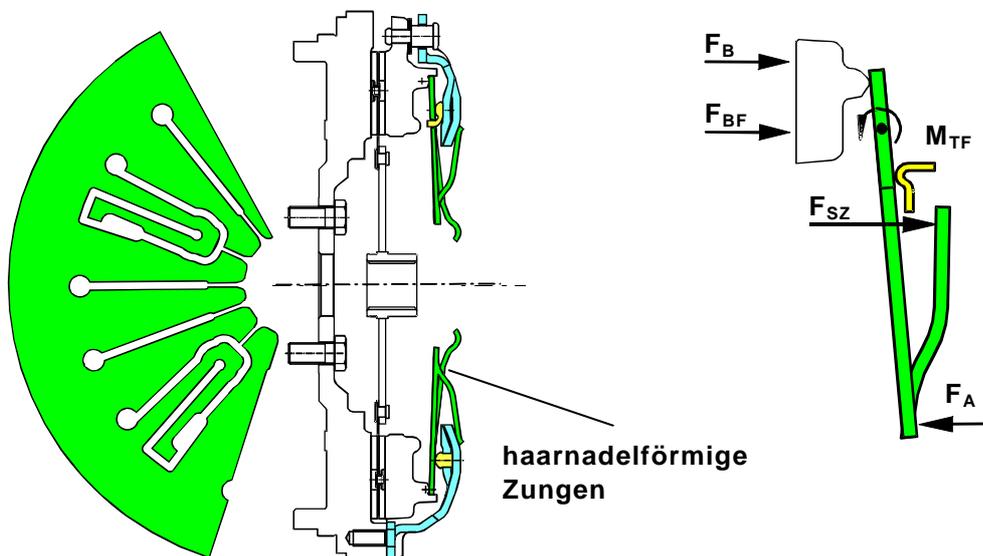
SAC mit Sensorkraft aus der Haupttellerfeder
